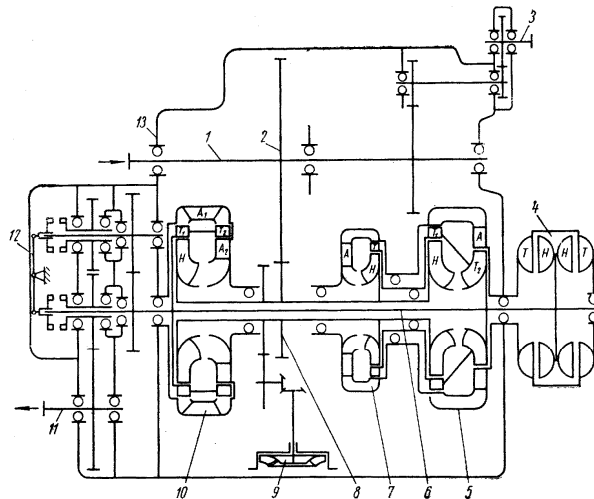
Кинематическая схема гидропередачи L830
